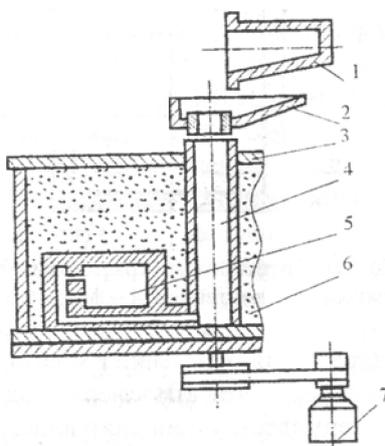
Схема заливочного контейнера: 1 - тигель; 2 - приемно-направляющий лоток; 3 - контейнер; 4 - центральный стоек; 5 - форма; 6 - наполнитель; 7 - привод
